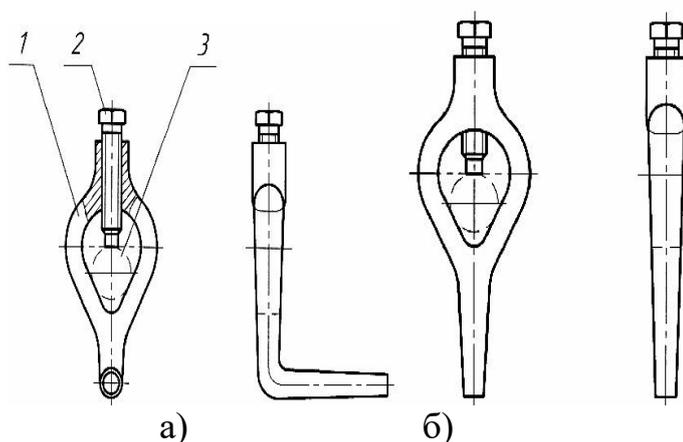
Типы токарных хомутиков: а) с отогнутым хвостовиком; б) с прямым хвостовиком. 1– корпус хомутика; 2– винт; 3– заготовка инструмента
